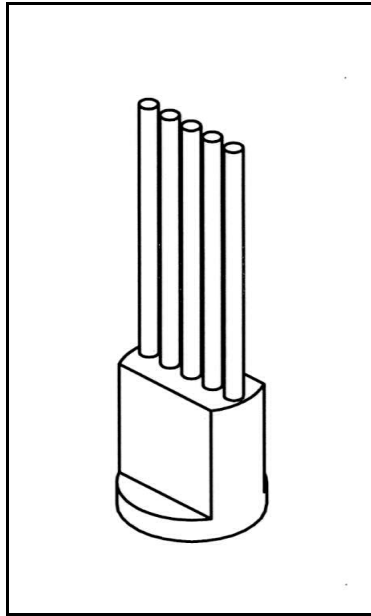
Desenho isométrico da conexão para a brasagem de conjuntos de cinco termopares.
